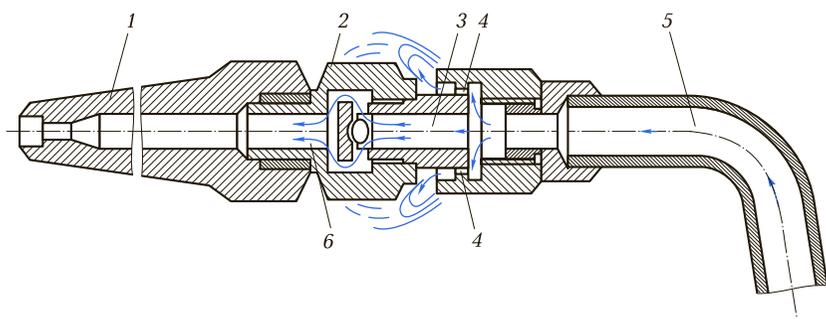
Конструкция наконечника с подогревателем для сварки на пропан-бутановой смеси:
